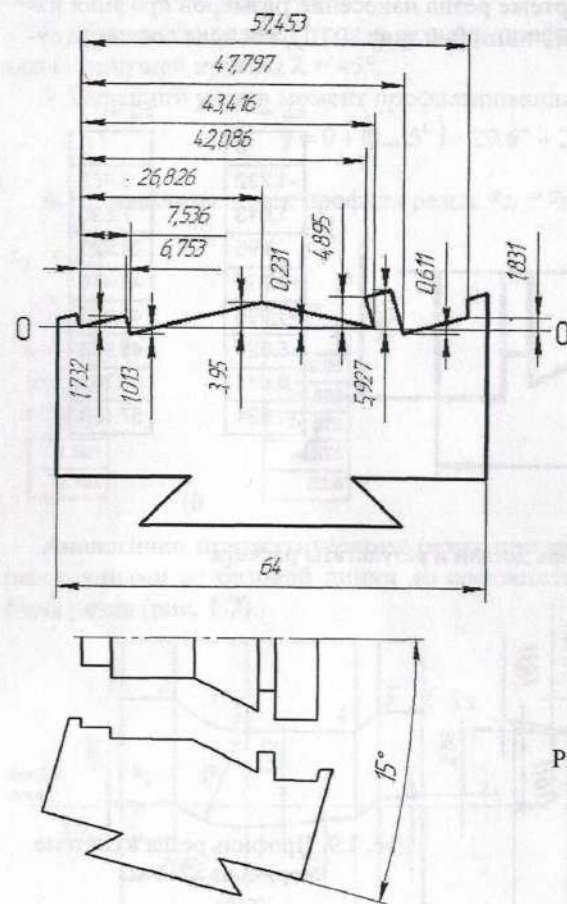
Нанесение размеров профиля на чертеже резца
